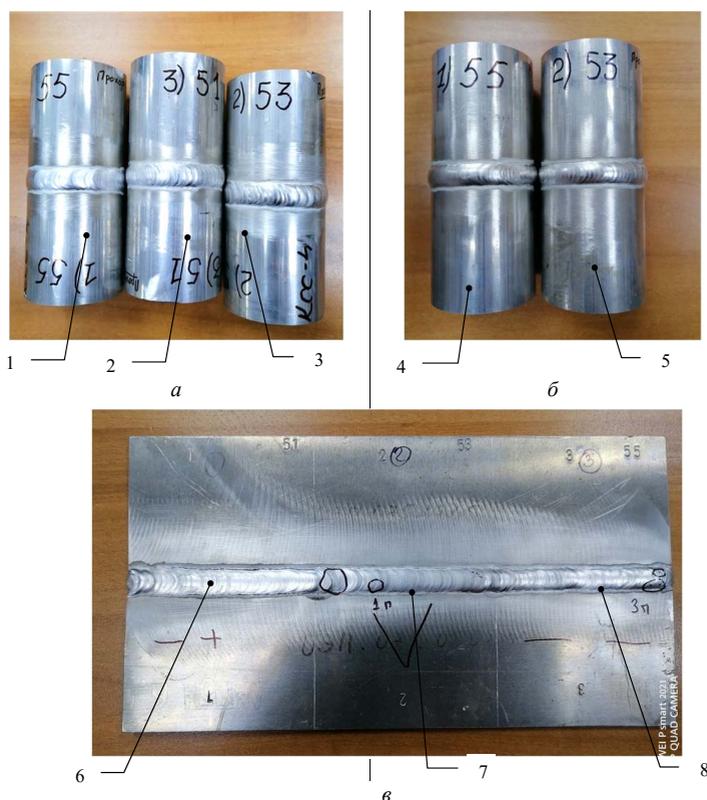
Образцы сварные, выполненные сварщиком № 1:
